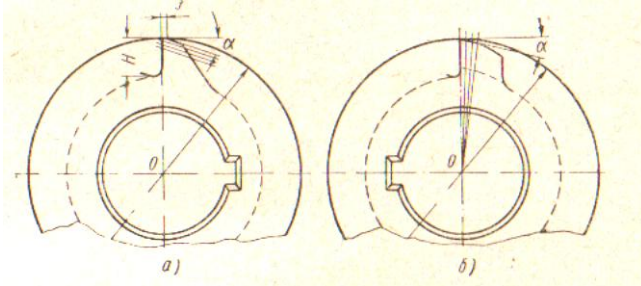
Конструкция зубьев фрезы: а- остроконечный зуб; б-затылованный зуб
